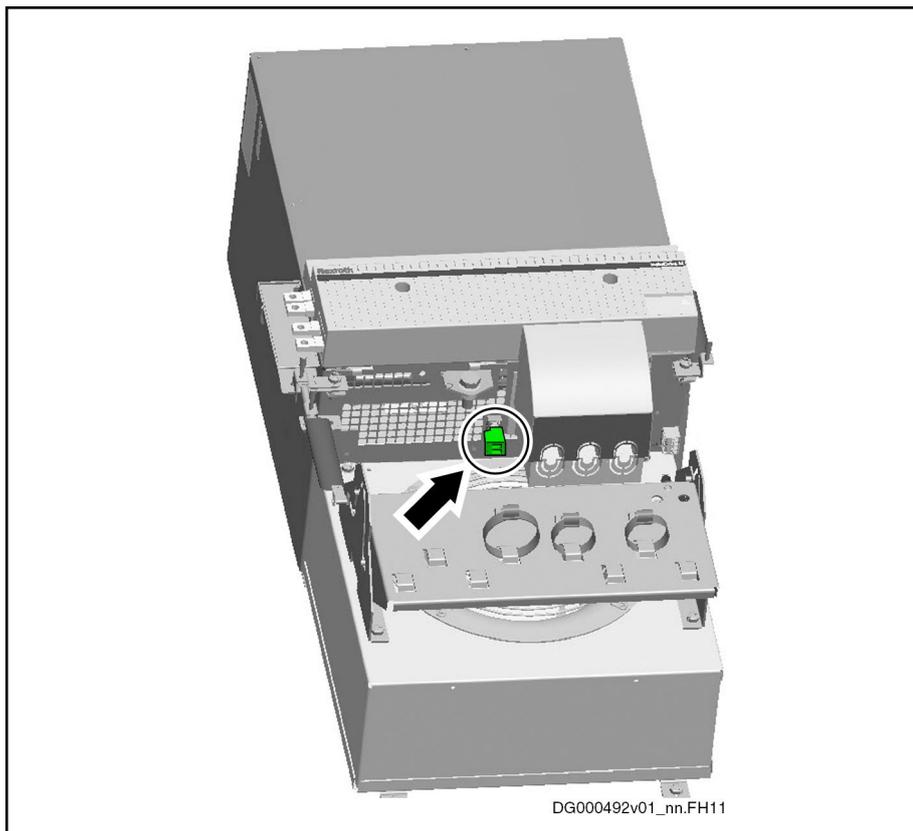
Collegamento X13 nella parte inferiore dell'apparecchio
